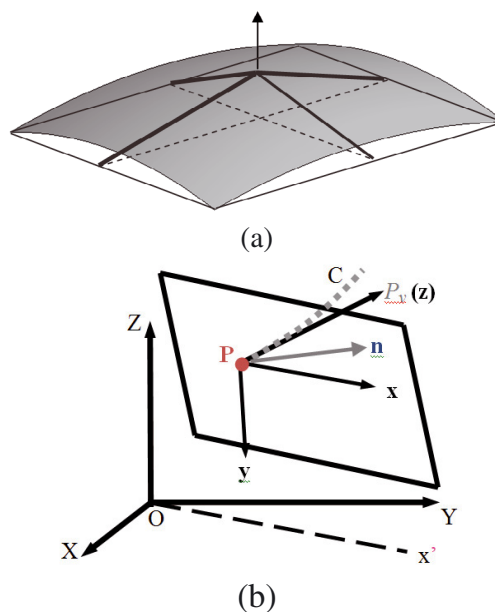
Surface sous serre flan et plan de travail. (a) SSSF bombée. (b) Plan de travail.
